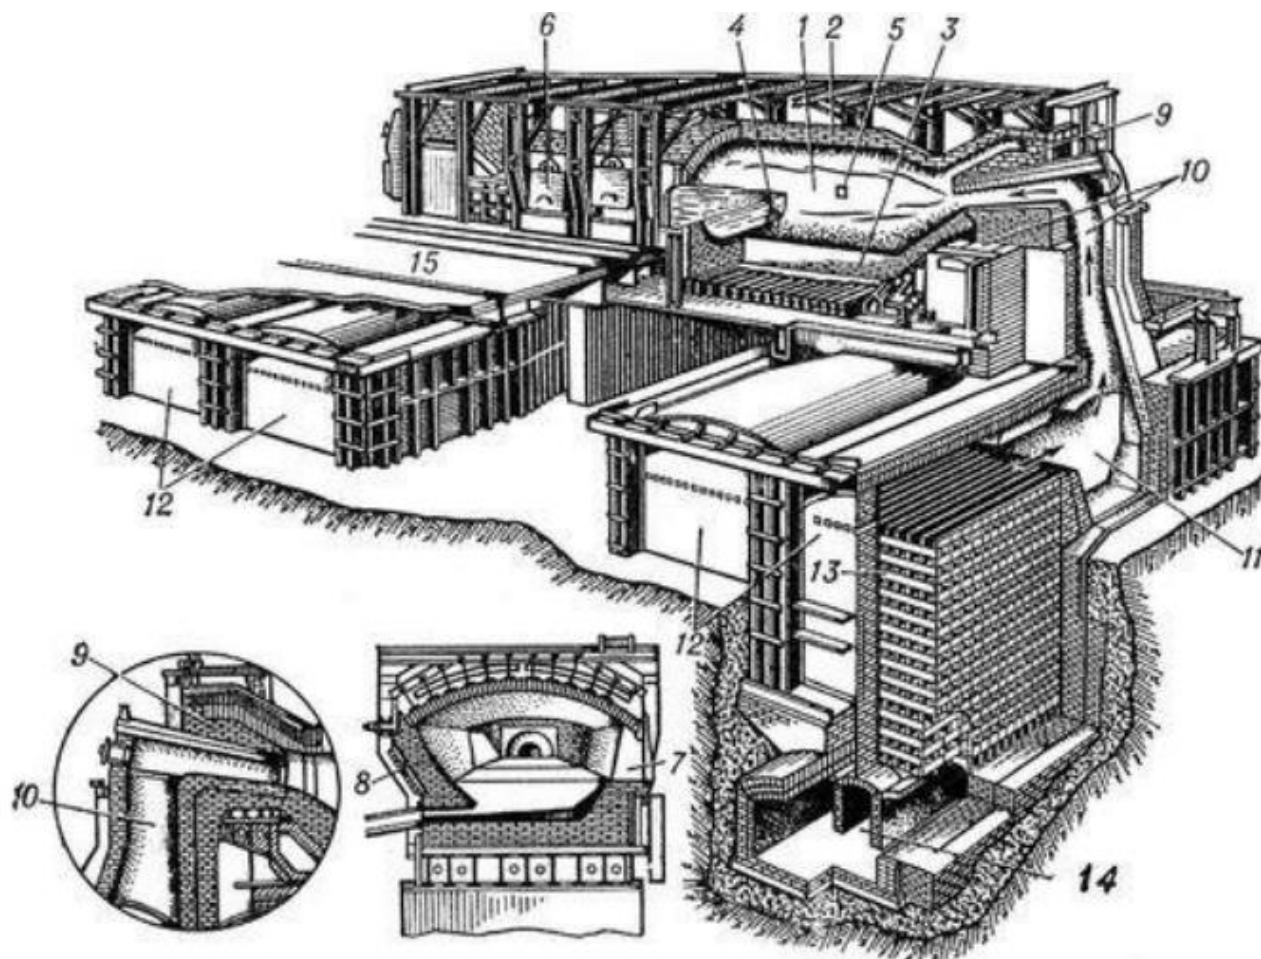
Конструкція мартенівської печі: 1- робочий простір печі; 2- звід печі; 3- подина печі; 4- отвір для випуску сталі; 5- отвір для спуску шлаку; 6- завалочні вікна; 7- передня стінка; 8- задня стінка; 9- головка печі; 10- вертикальні канали; 11- шлаковики; 12- регенератори; 13- насадка регенераторів; 14- борова; 15- робочий майданчик.
